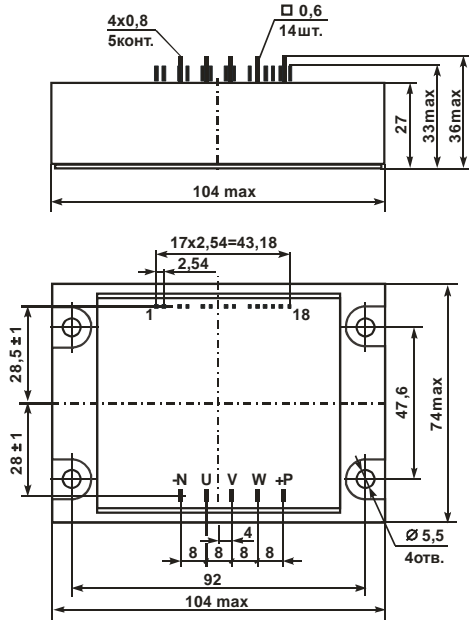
Габаритный чертеж модулей: M13A-10-1
